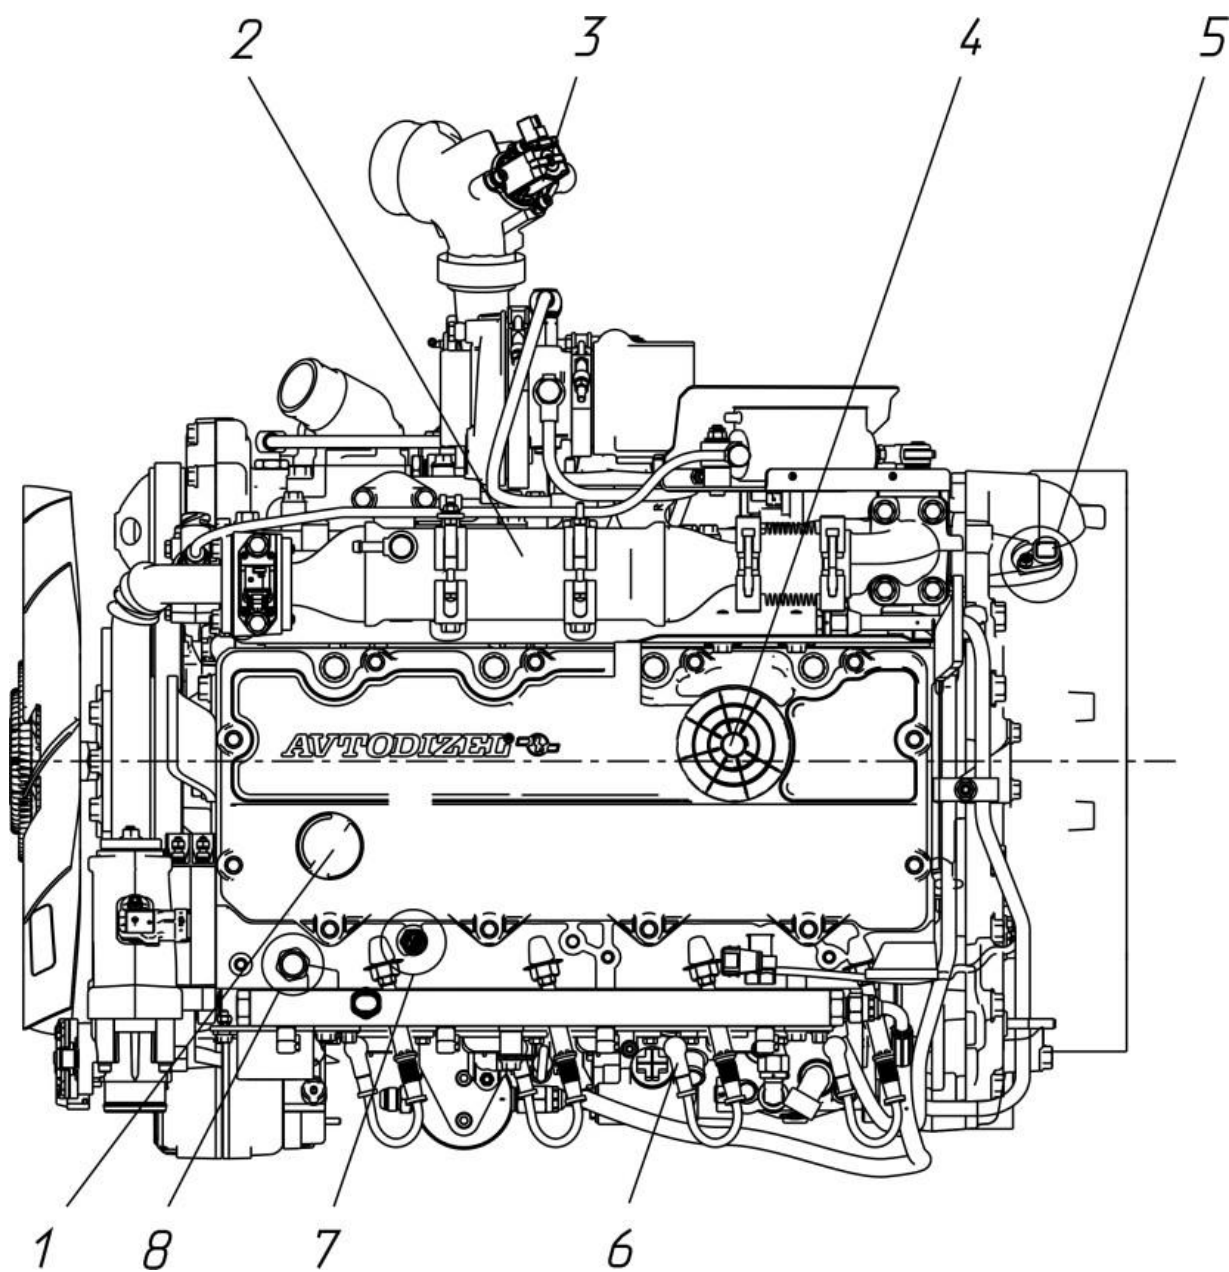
д – Расположение агрегатов и узлов двигателя ЯМЗ-53444-20 (вид сверху):
